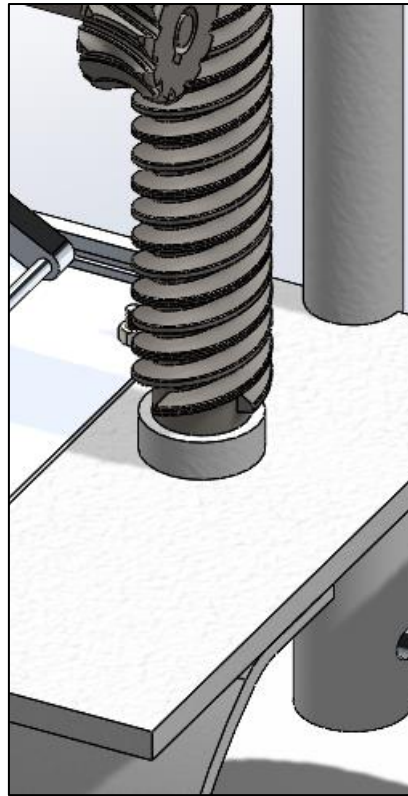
Soporte de la base del agarre del carro para el tornillo sin fin. Fuente propia.
